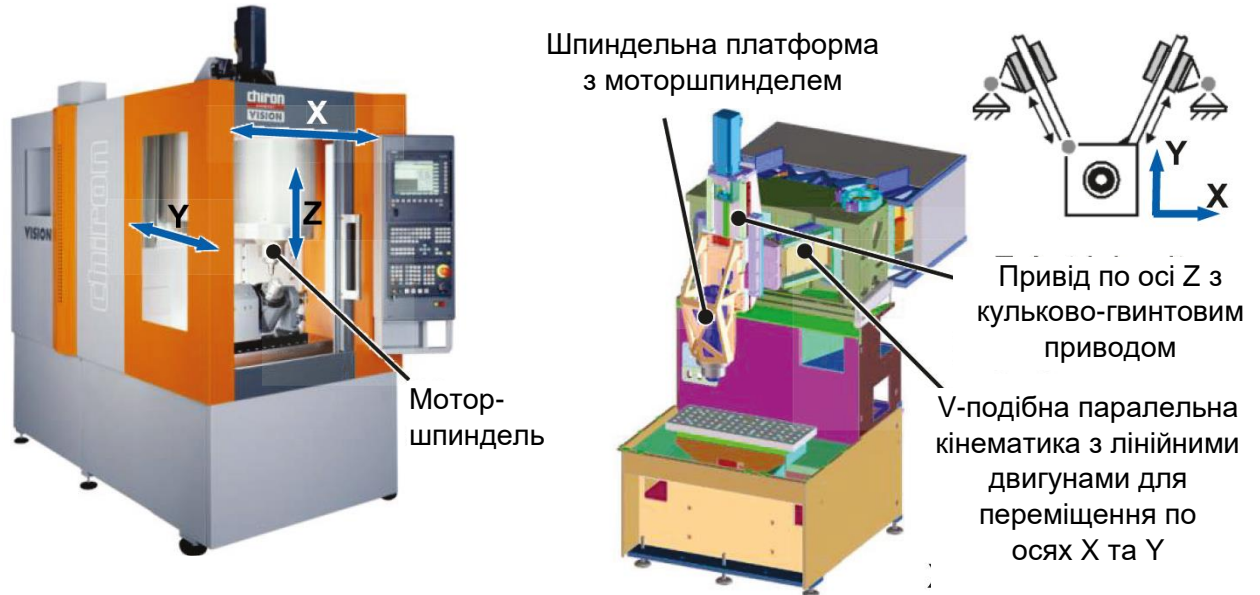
Високошвидкісний обробний центр з V-подібною паралельною кінематикою фірми CHIRON Werke
